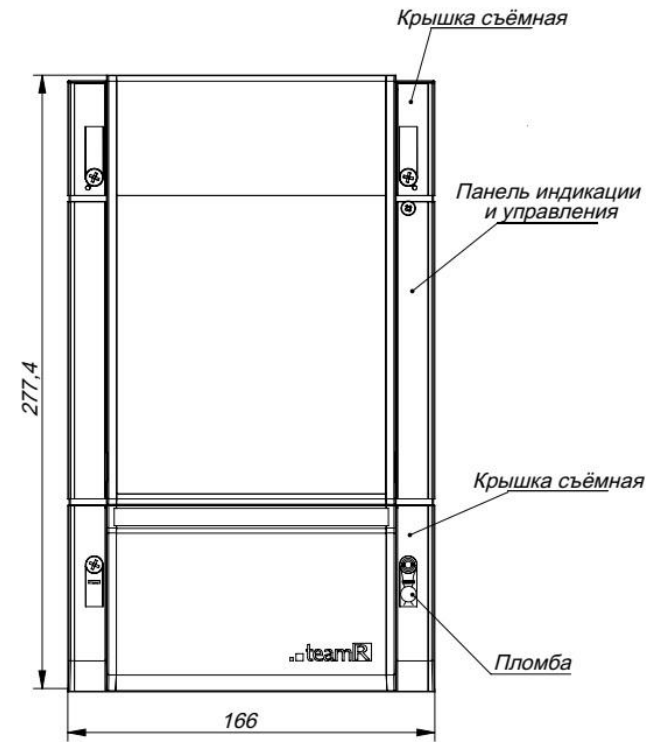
Габаритные размеры и вид счетчика со стороны крепления
